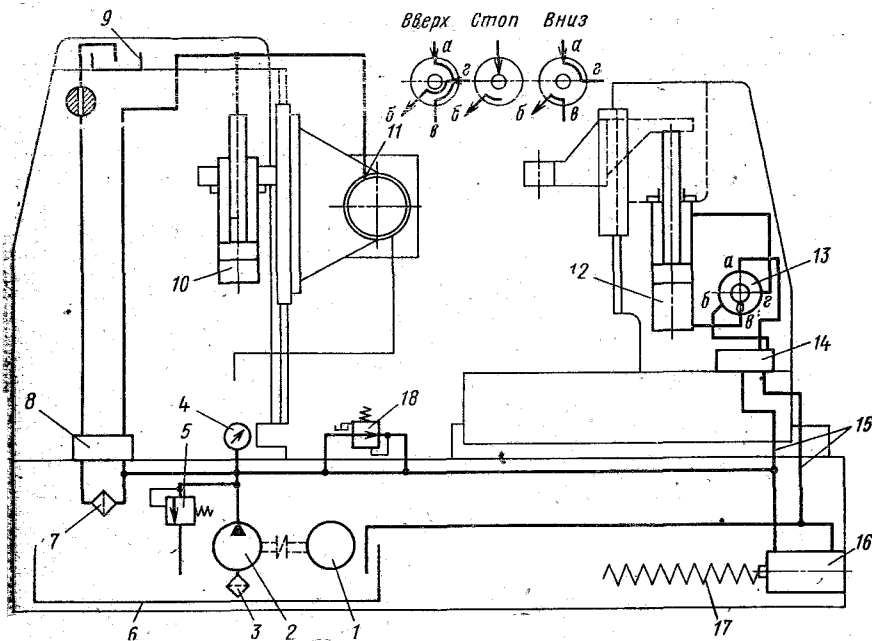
Гидравлическая схема зубофрезерного станка мод. 5Е32;
